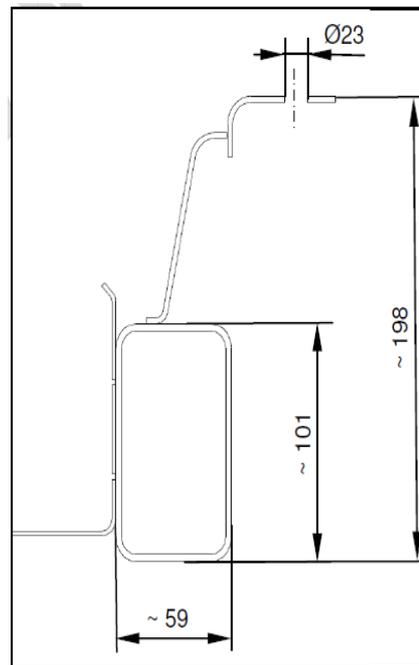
coupe T-T (Amarok SC/DC)
